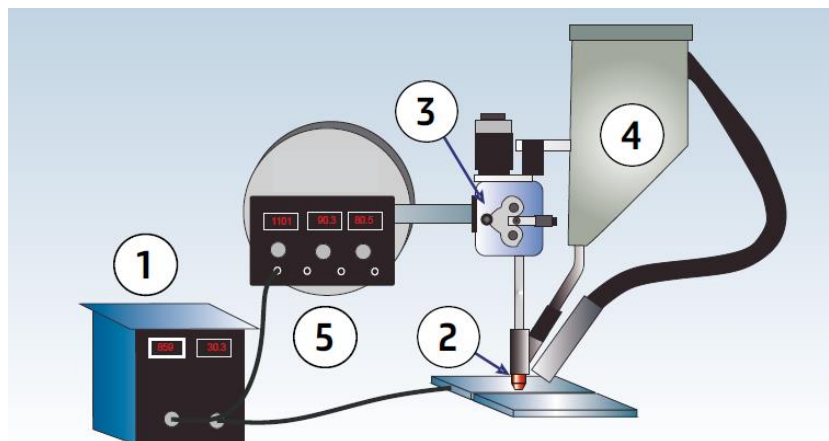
Representação esquemática dos componentes básicos do equipamento de soldagem a arco submerso
